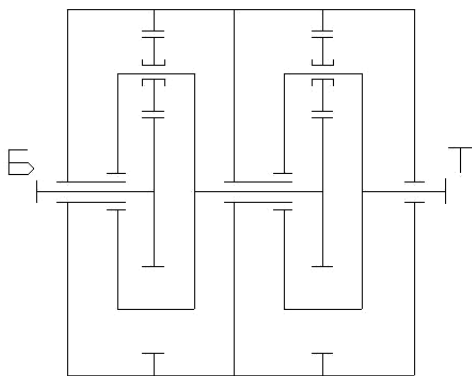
Двухступенчатый планетарный редуктор (2КН)
